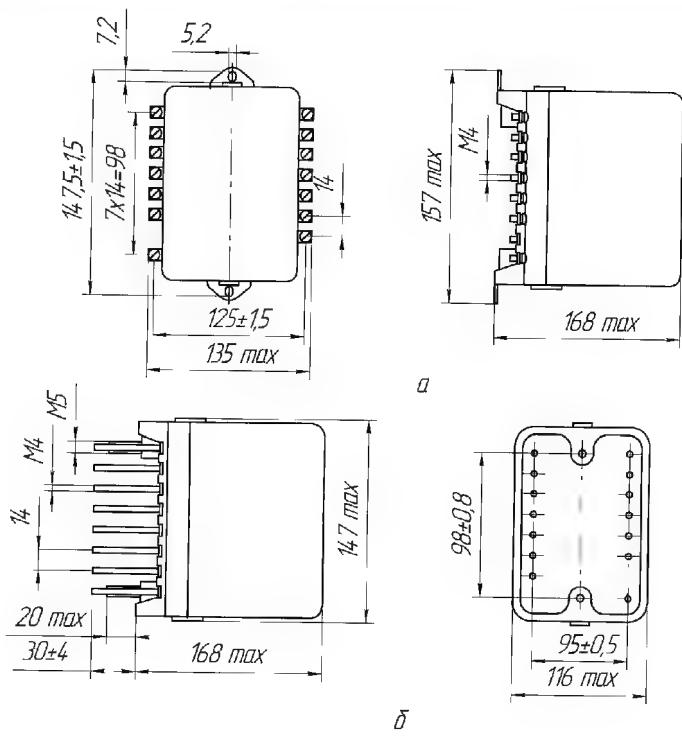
Габаритные, установочные и присоединительные размеры защиты типа ЗЭП 1.
